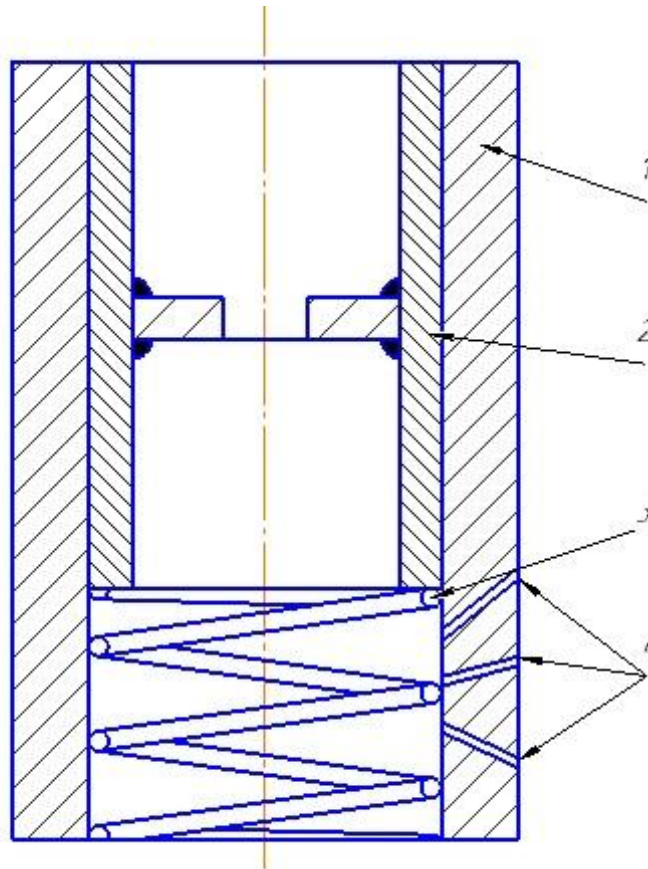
Схема калибратора: 1-корпус; 2-втулка; 3-пружина; 4-отверстия;
